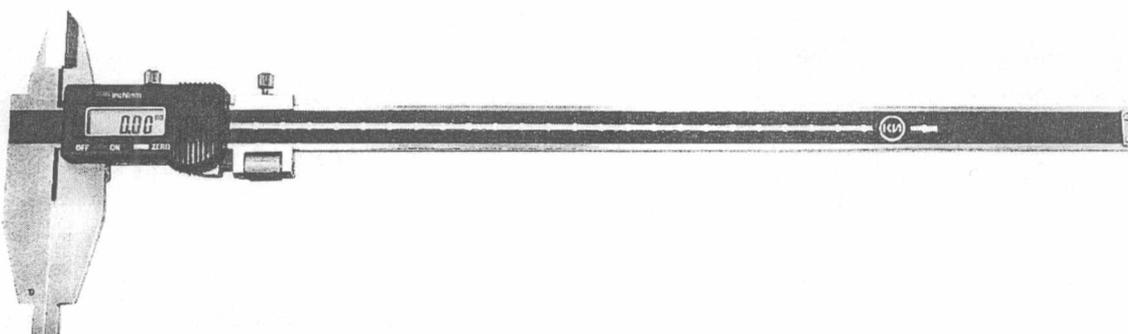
Общий вид штангенциркулей типа ШЦЦ-II
